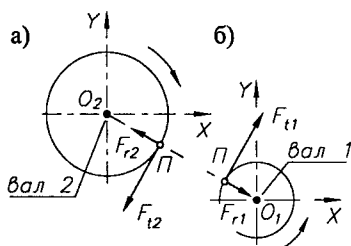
Схемы сил F_t и F_r , нагружающих валы: а) зубчатого колеса; б) шестерни
